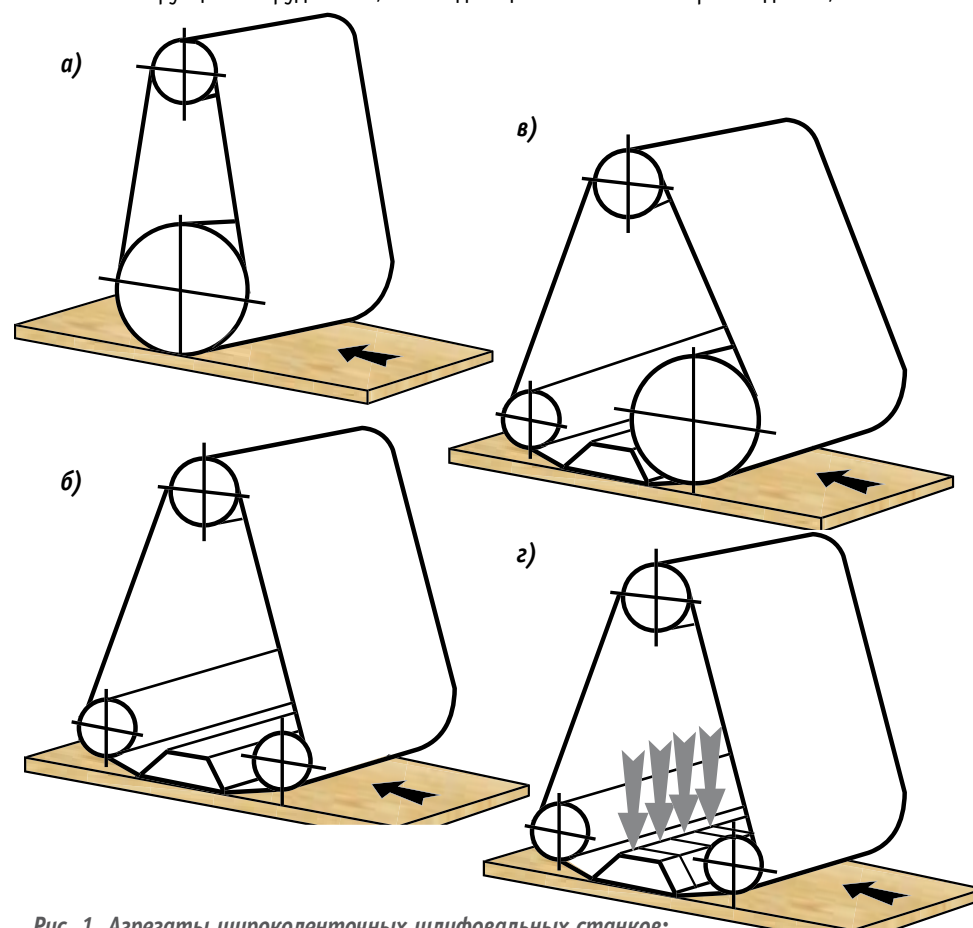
Агрегаты широколенточных шлифовальных станков:
